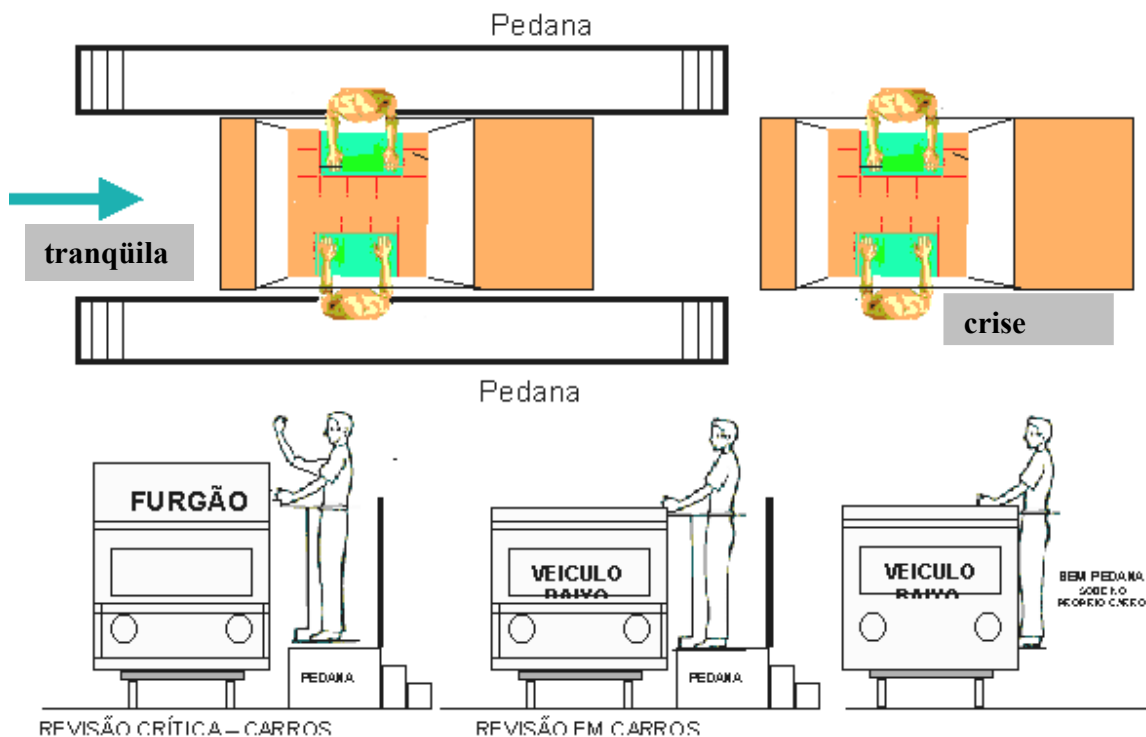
Revisores de teto – Ilustração das situações “tranqüilas” e “crise”
